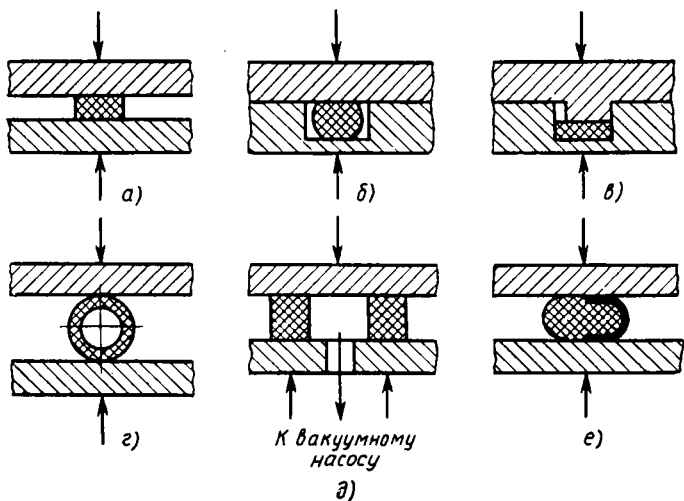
Конструктивные схемы разборных вакуумных соединений с полимерными уплотнителями
